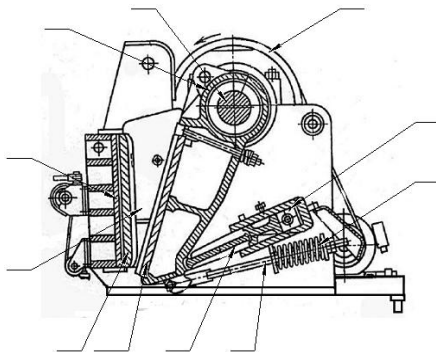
Конструкция щековой дробилки со сложным качанием щеки
